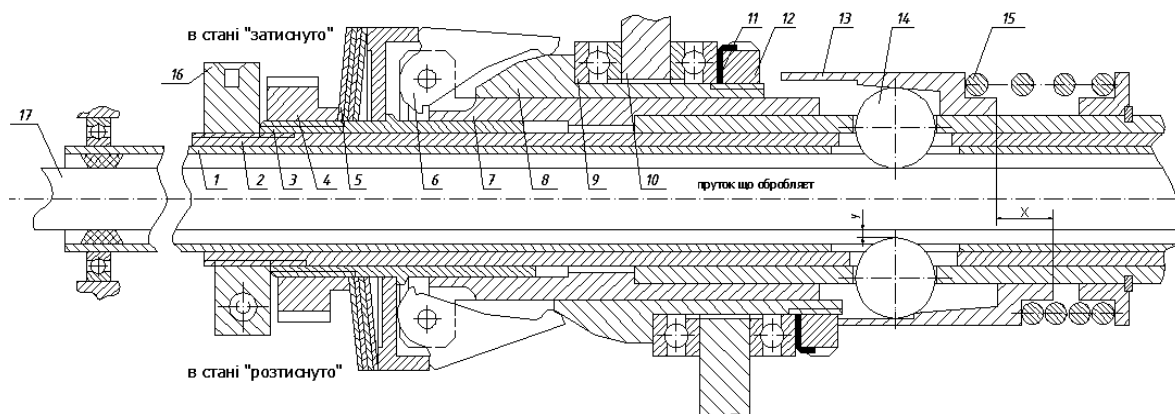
Механізм додаткового затиску прутка в складі шпиндельного вузла багатшпиндельного токарного автомата мод. 1Б240
